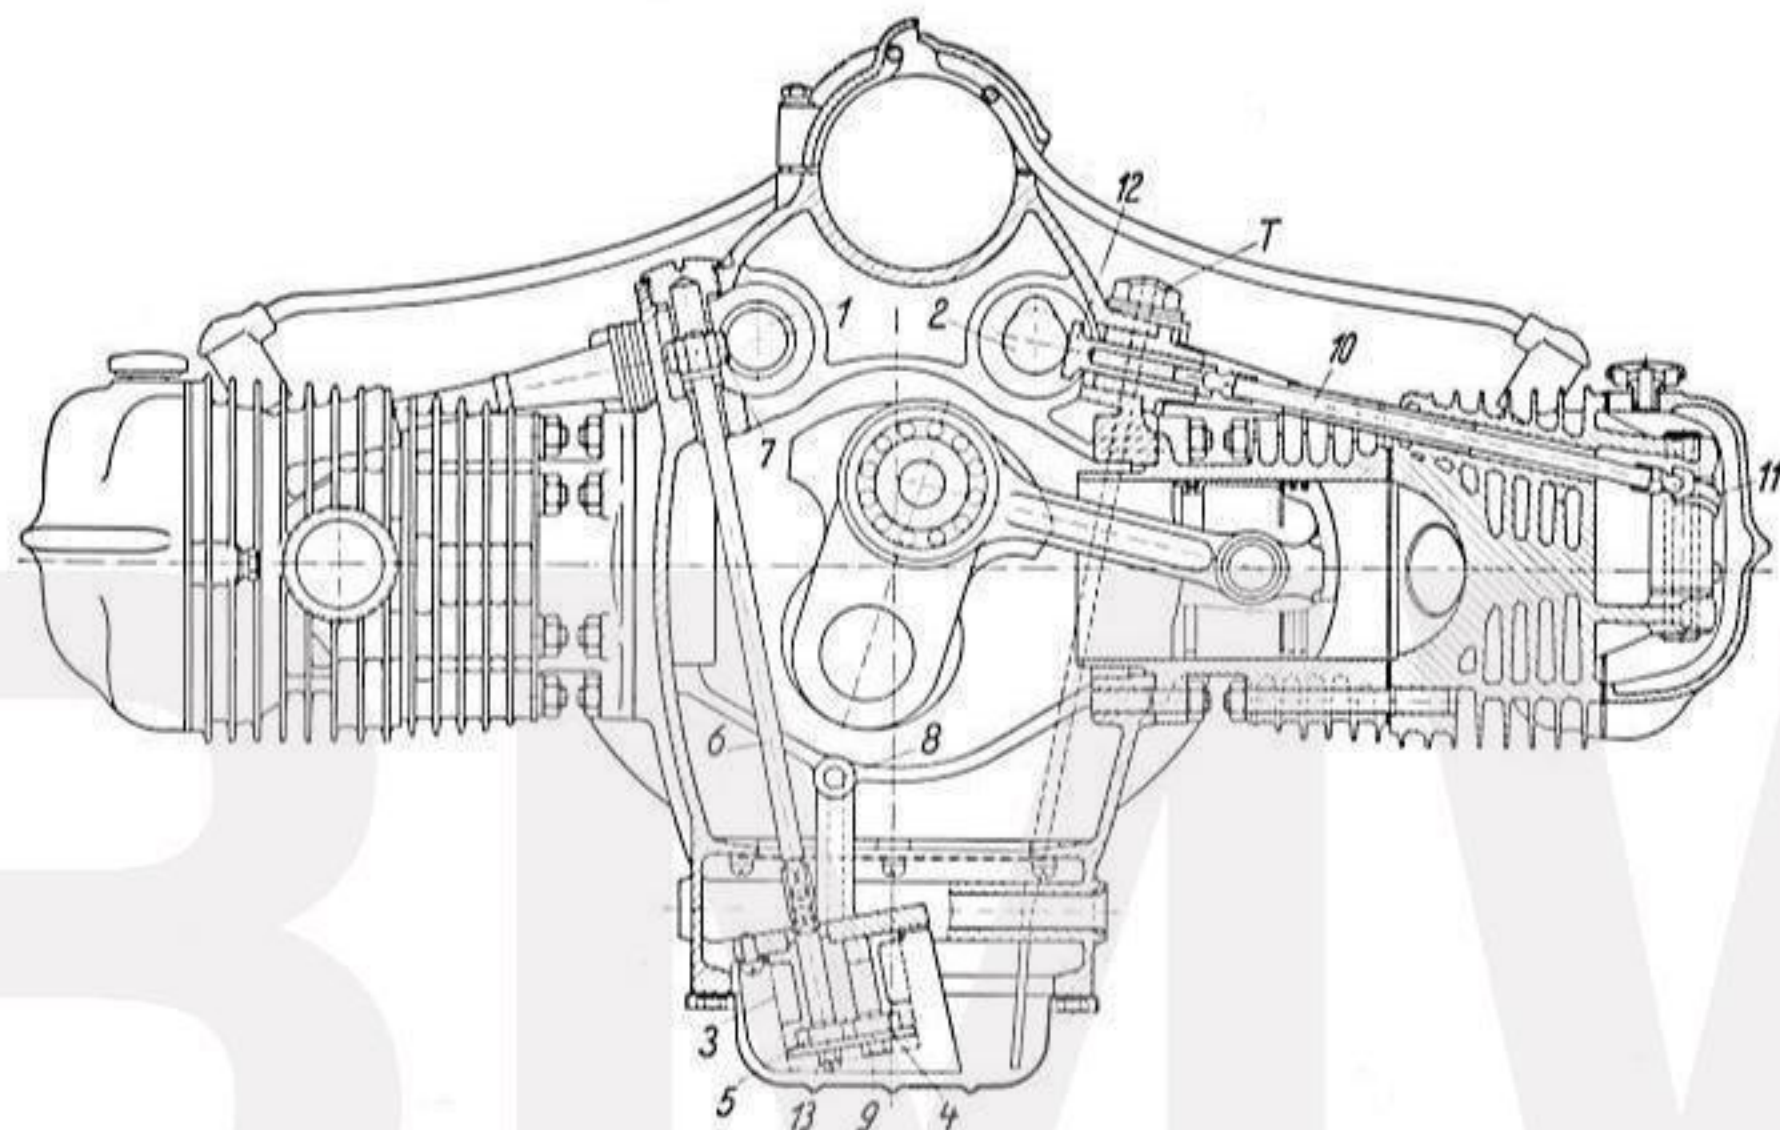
R 5-Motor mit teilweisem Querschnitt durch die Zylindermitte (die Bezeichnung der Ölpumpenteile gilt ebenso für den R 6-Motor)
